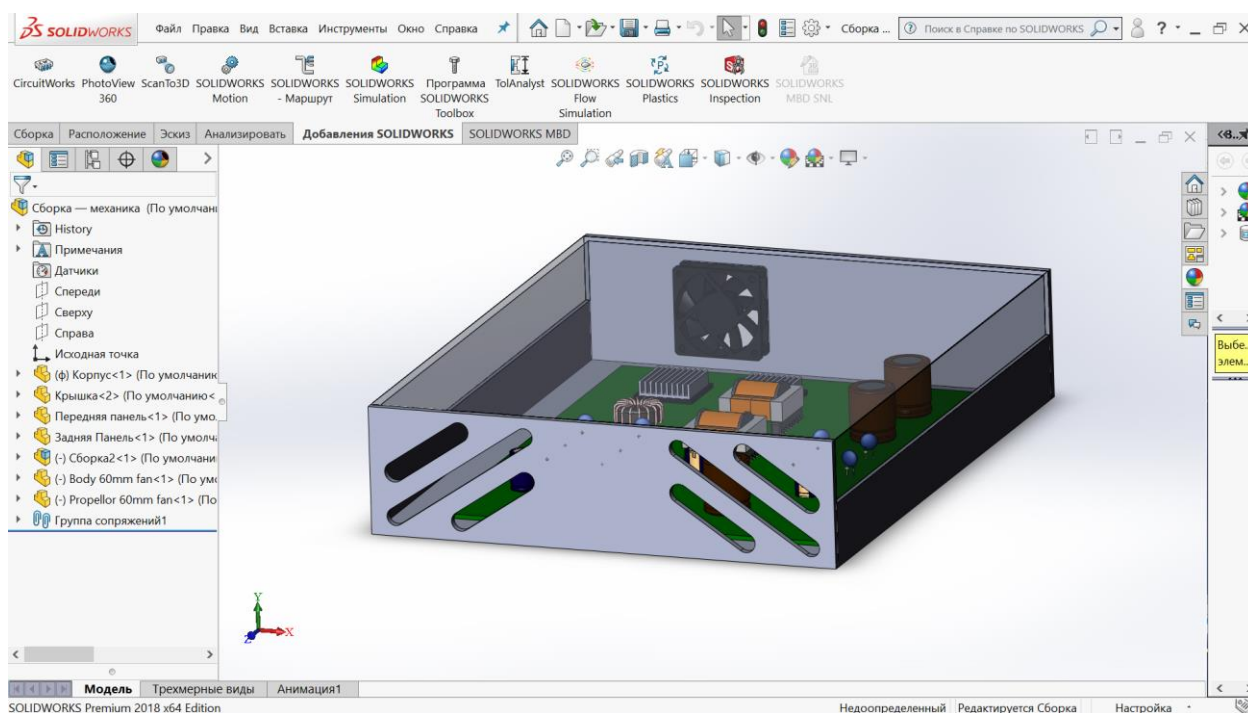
Конструкция деталей и сборок «Преобразователя напряжения».
